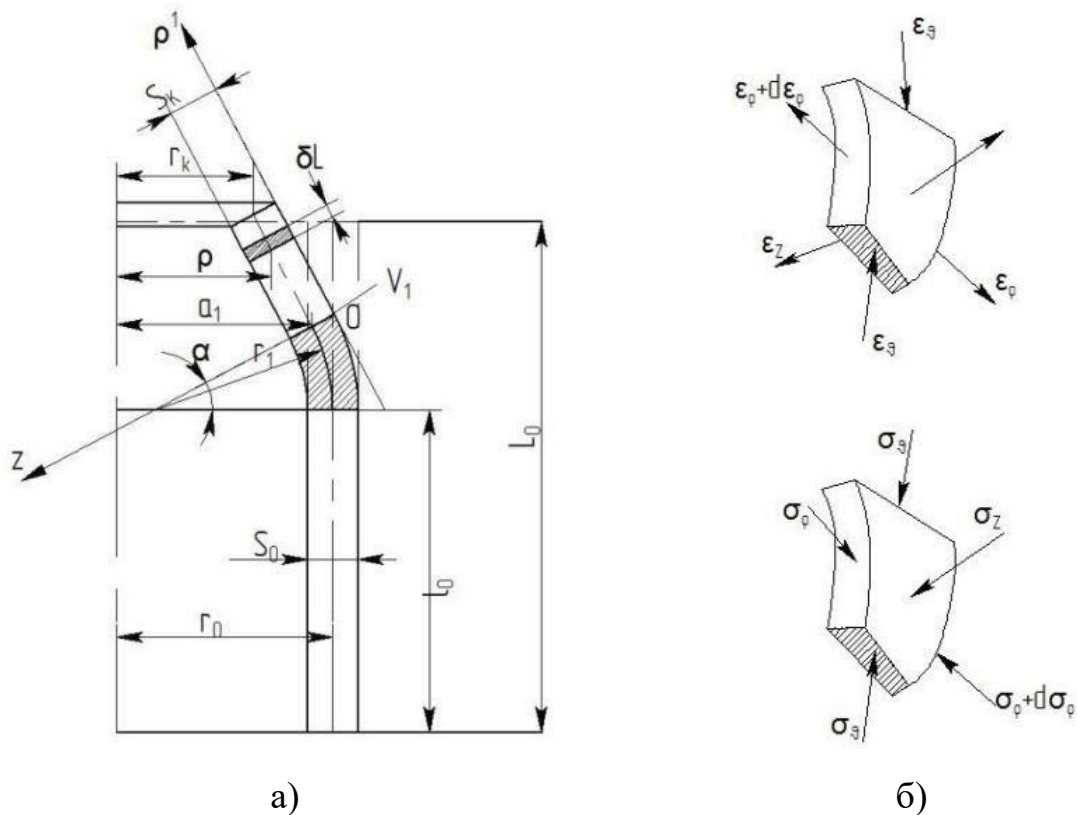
Формозміна трубної заготовки операцією обтиску:
